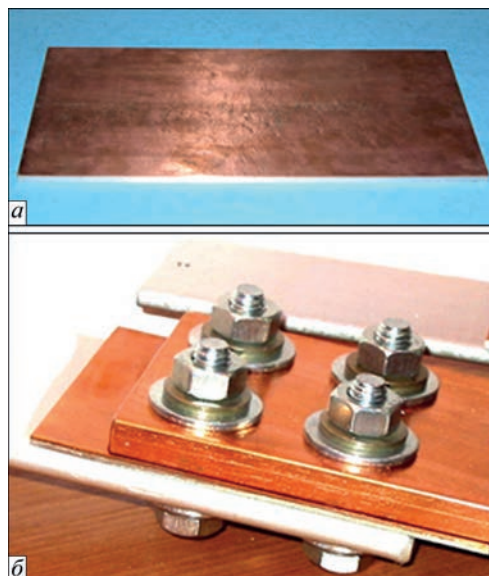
Біметалева Al–Cu пластина (а) і загальний вигляд з'єднання алюмінієвої і мідної шини через вставку (б)
